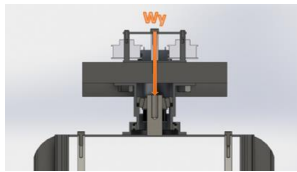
Carga sobre el rodamiento de rodillos superior.
